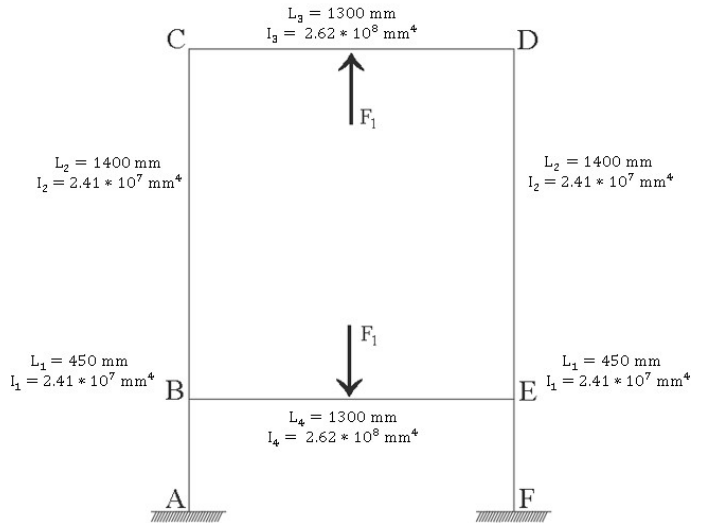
Estructura del Pórtico de la Prensa Hidráulica de 100 t.
